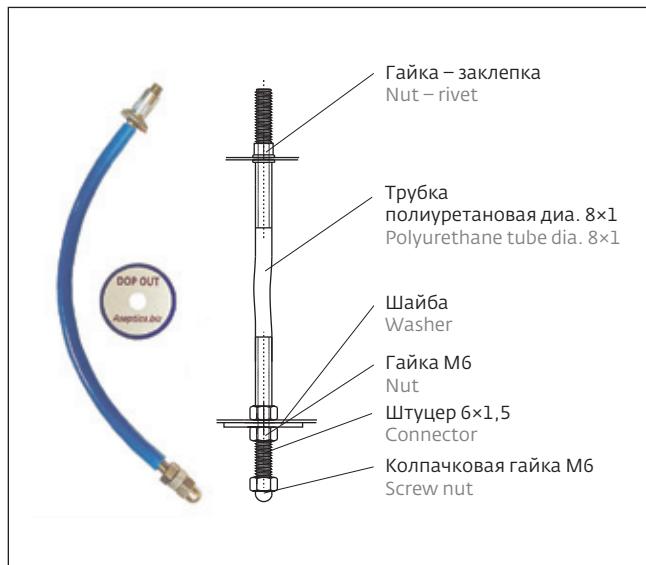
DOP OUT порт: слева: внешний вид устройства; справа: чертеж
